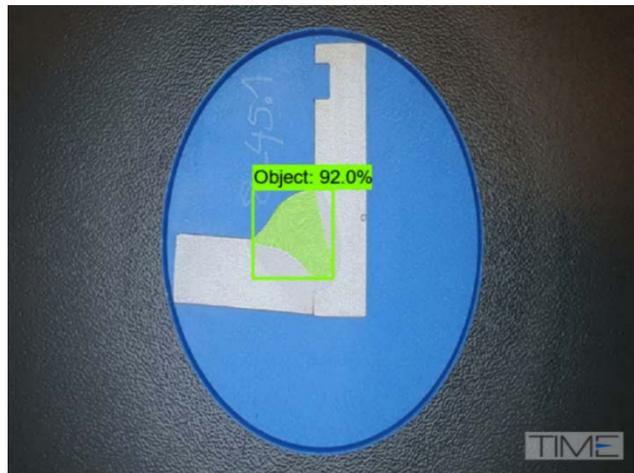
Beispiel für die Segmentierung des Schweißguts am Querschliff einer MAG-Kehlnaht.
